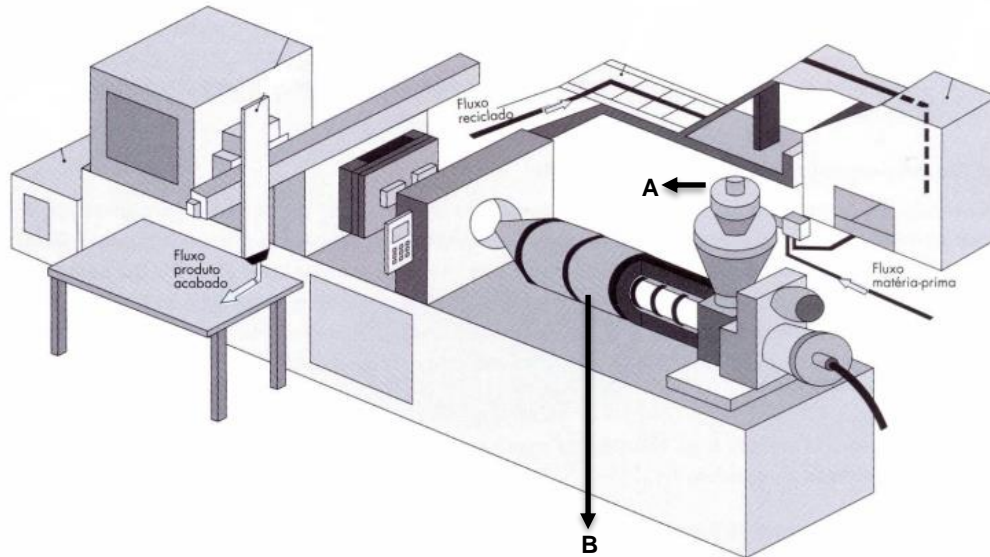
Exemplo de uma máquina de injeção de moldes: A-Tremonha; B- Cilindro da máquina⁵.
